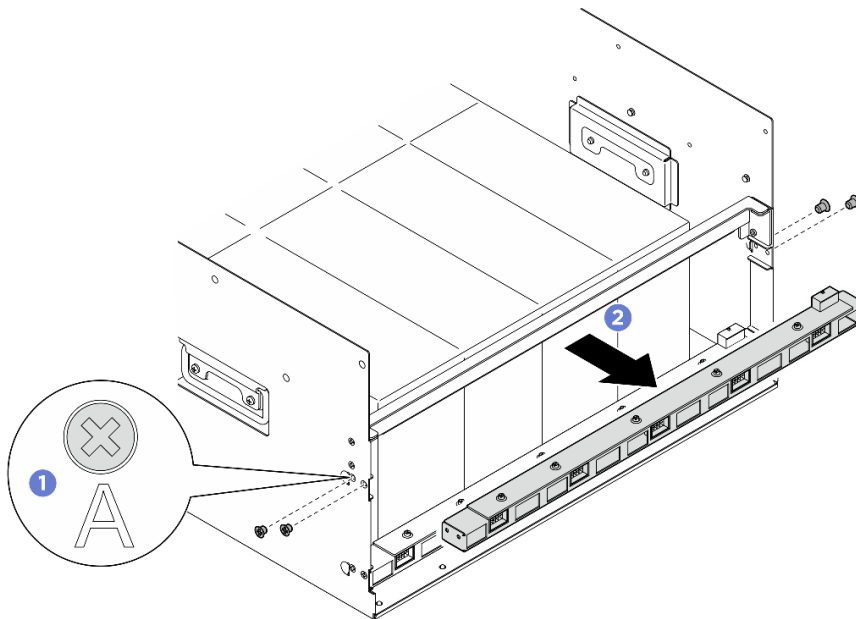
Entfernen der hinteren Lüfterplattenbaugruppe
